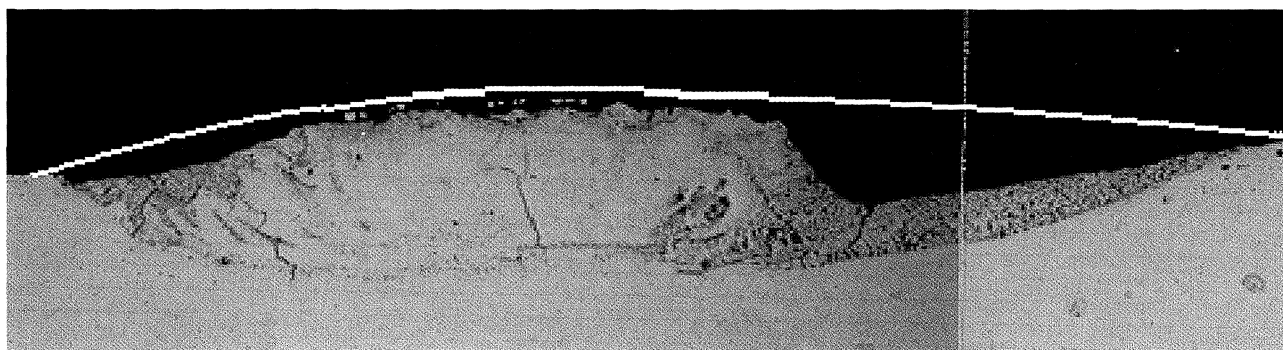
Secção transversal da Pista 2.5 (50×).
